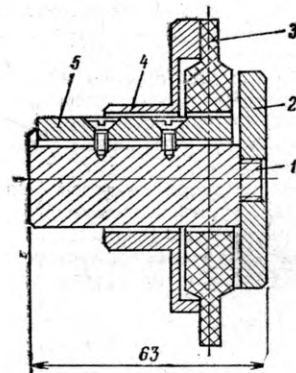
Разметка кулачковой шайбы с помощью шаблона: 1 — вал; 2 — диск; 3 — заготовка; 4 — шаблон; 5 — шпонка
